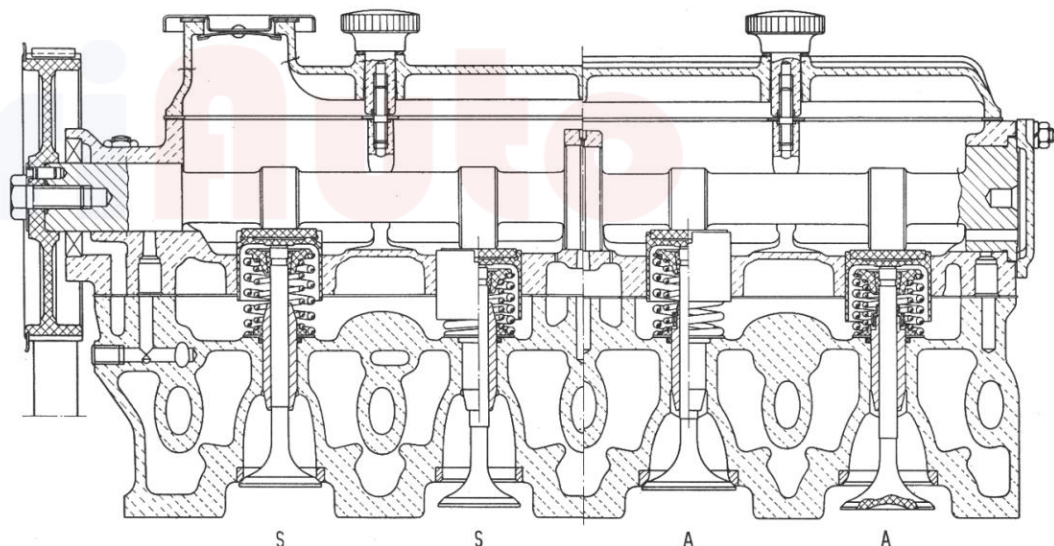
Längsschnitt durch den Zylinderkopf.
